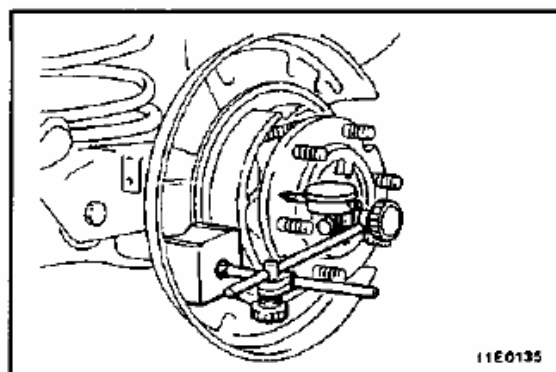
Проверка вала привода заднего колеса на наличие люфта
